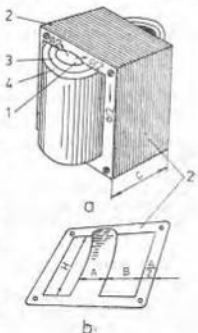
Transformator monofazat în manta cu tole din întregul: a — transformatorul (vedere); b — tola miezului: 1 — spațiu prevăzut în carcasa bobinei pentru împachetarea miezului; 2 — tola miezului; 3 — bobină primară; 4 — bobină secundară.
